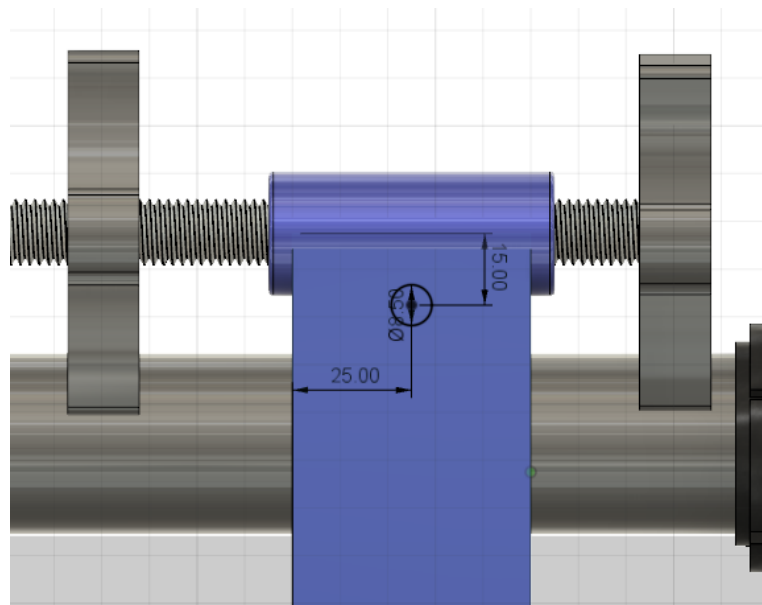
Kennzeichnung und Bemaßung des 8,5-mm-Bohrloches für die Ringmutter am Rollentrainer
